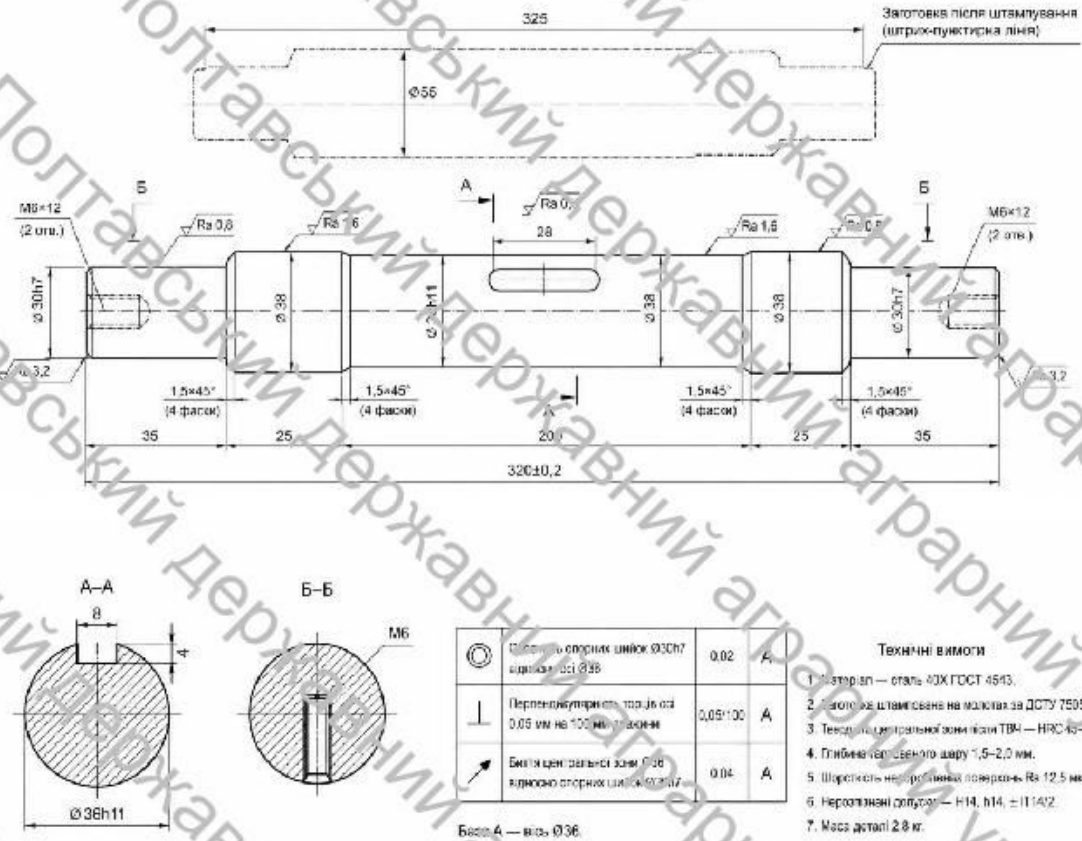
Робочий креслення осі повороту секції штанги обприскувача
